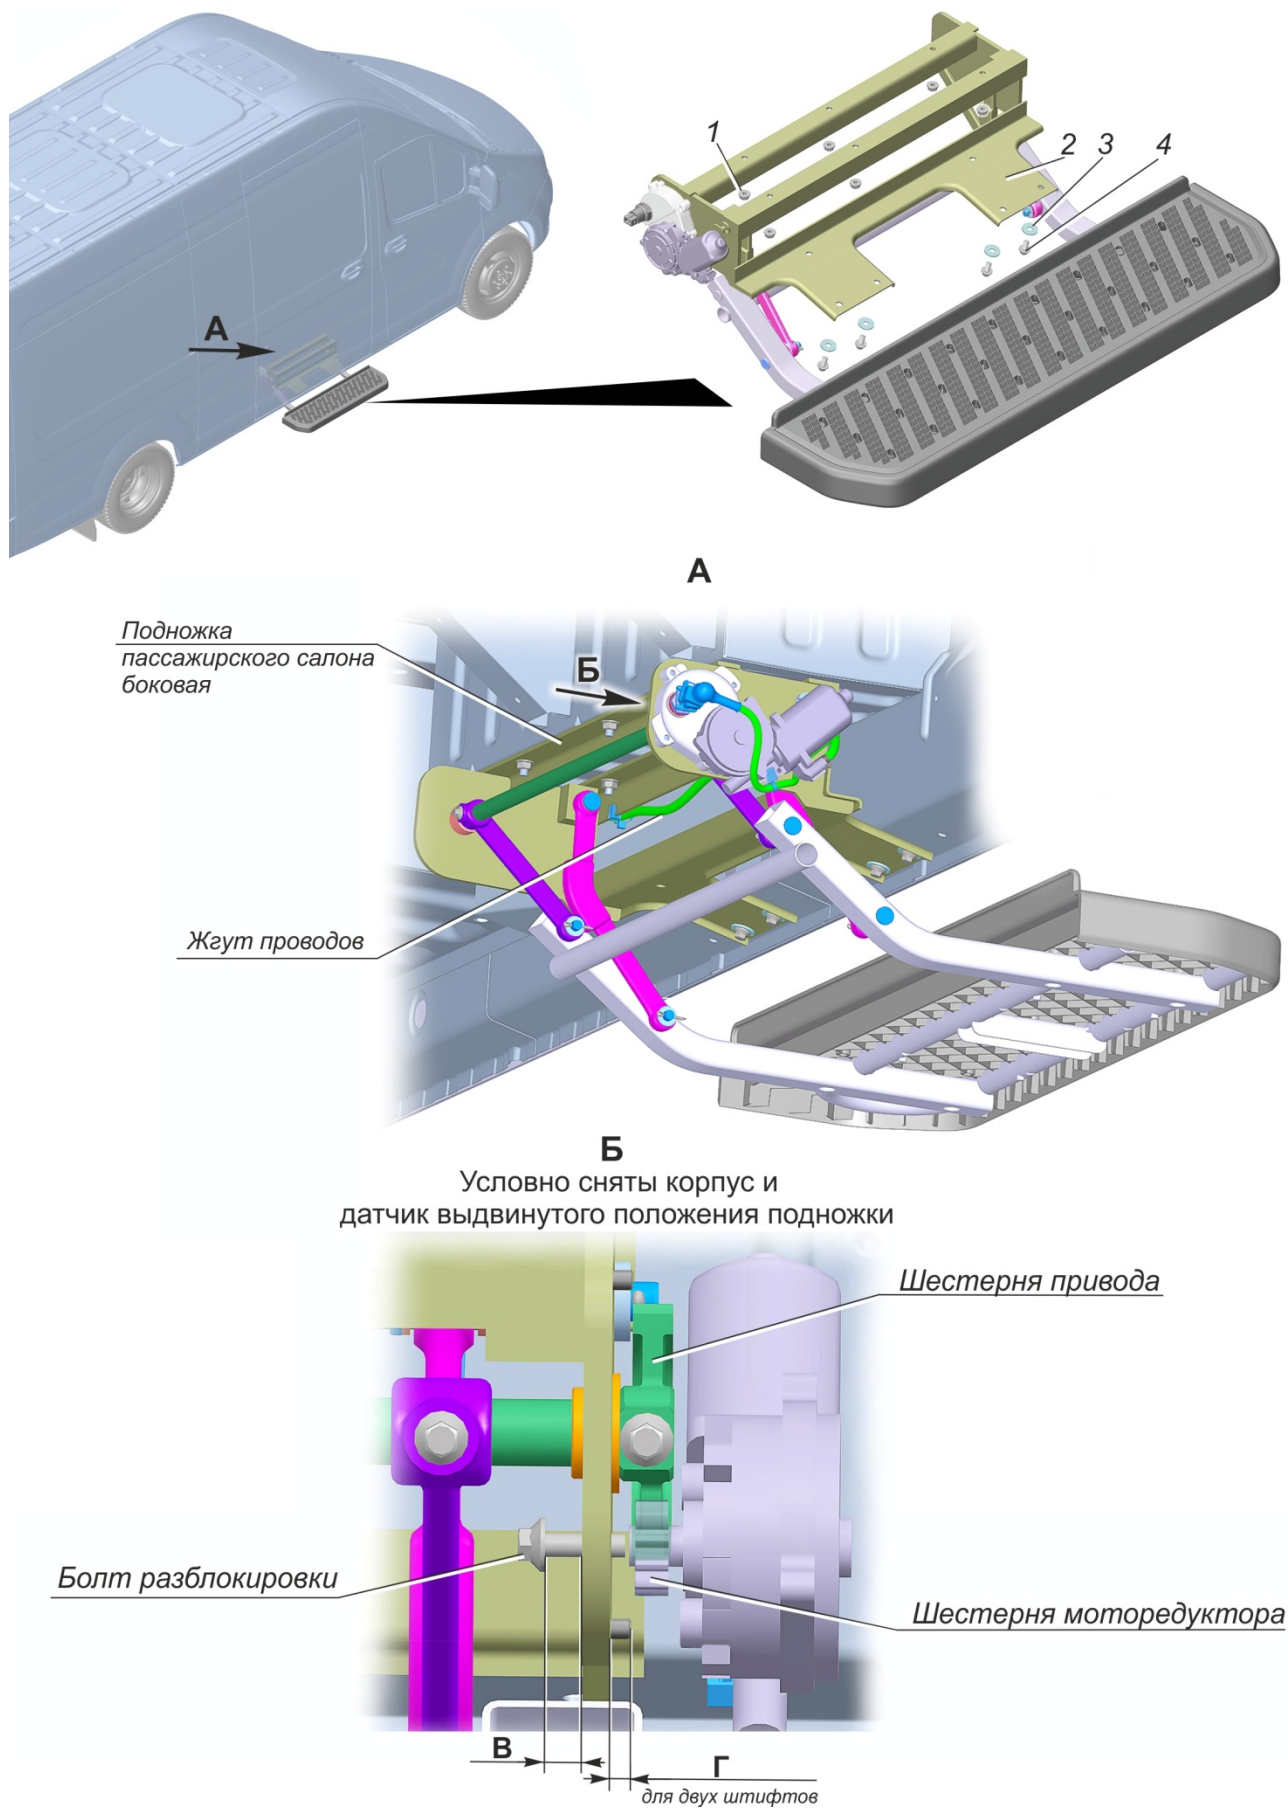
Установка выдвигной подножки: В=8,5-9,5 мм; Г= 5,0-5,5 мм; 1 – гайка; 2 - подножка выдвигная; 3 – шайба; 4 - болт
